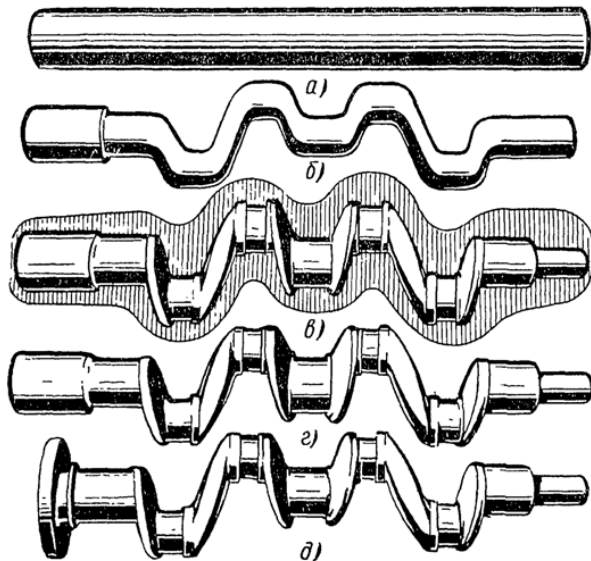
Формообразование заготовки коленчатого вала при штамповке на механическом прессе:
